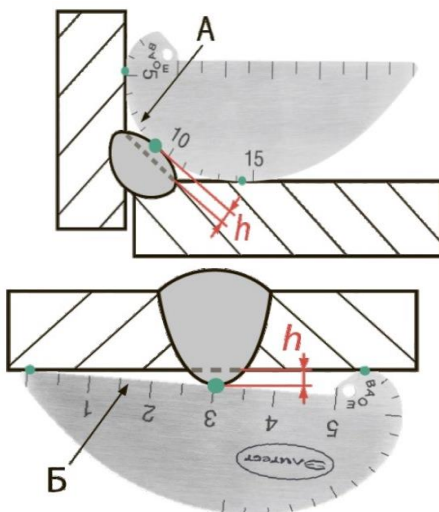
Контроль тавровых (А) и стыковых (Б) сварных соединений.
